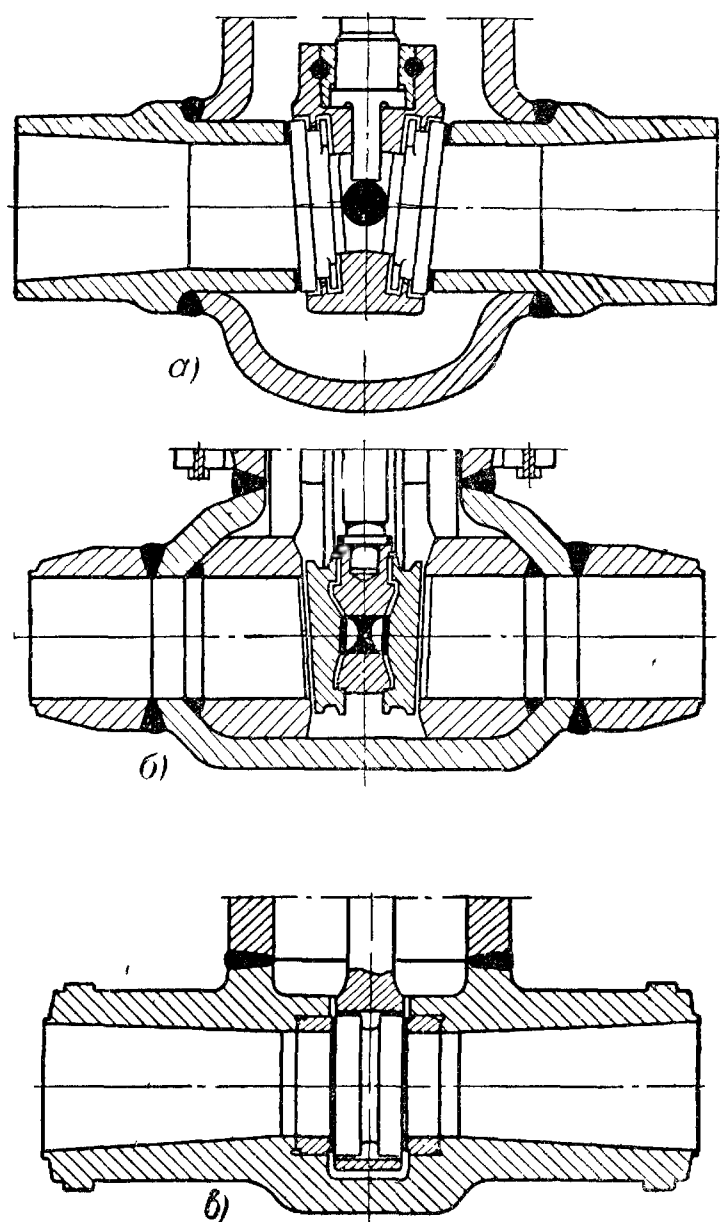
Некоторые конструкции сварных корпусов задвижек.
